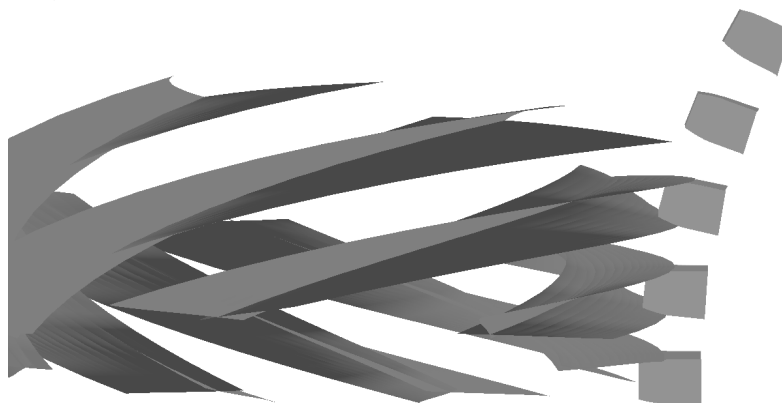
OpenGL промальовка в Eclipse SDK зачеплення гіперболоїдного шліфувального круга й циліндричного зубчастого колеса
